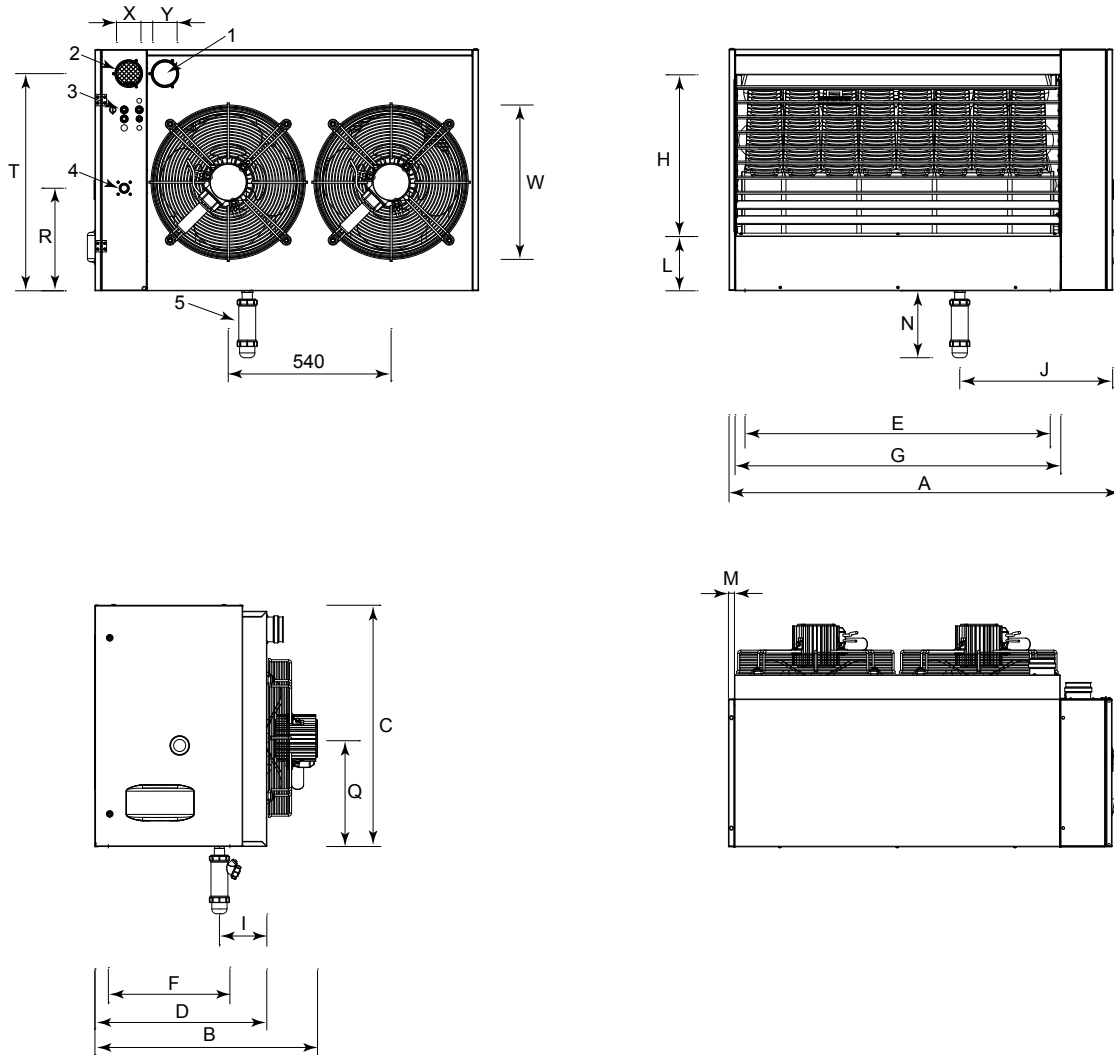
Abmessungen Warmlüfterzeuger G30, G45, G60
